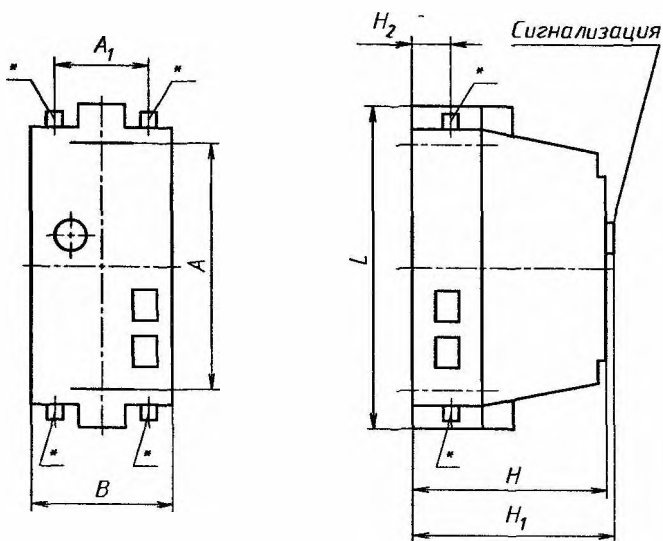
Габаритные и установочные размеры реверсивных пускателей ПМЛ 1-й и 2-й величин в оболочке
